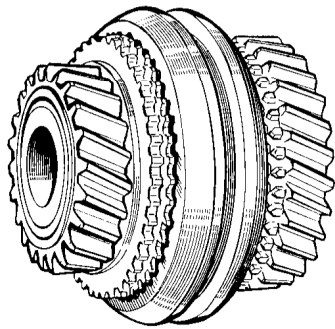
Ступица муфты синхронизаторов III и IV передач с муфтой включения синхронизаторов и набором шестерен (перед установкой в картер коробки передач)
